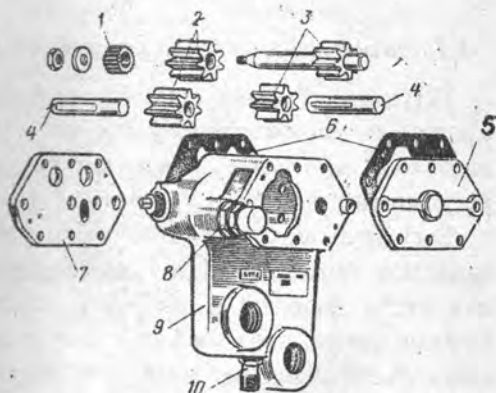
Детали масляного насоса МШ-8М: 1-шлицевая муфта; 2-шестерня откачивающей ступени; 3-шестерня нагнетающей ступени; 4-ось ведомой шестерни; 5-крышка корпуса насоса; 6-паронитовая прокладка; 7-опорный фланец; 8-редукционный клапан; 9-корпус; 10-штуцер приемника термометра
